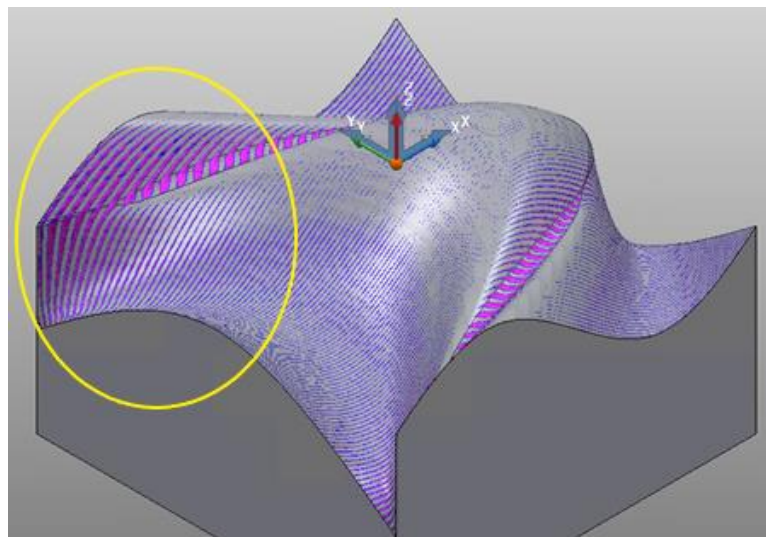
Zobrazení vytvořené hranice pro kulovou frézu D8 mm
